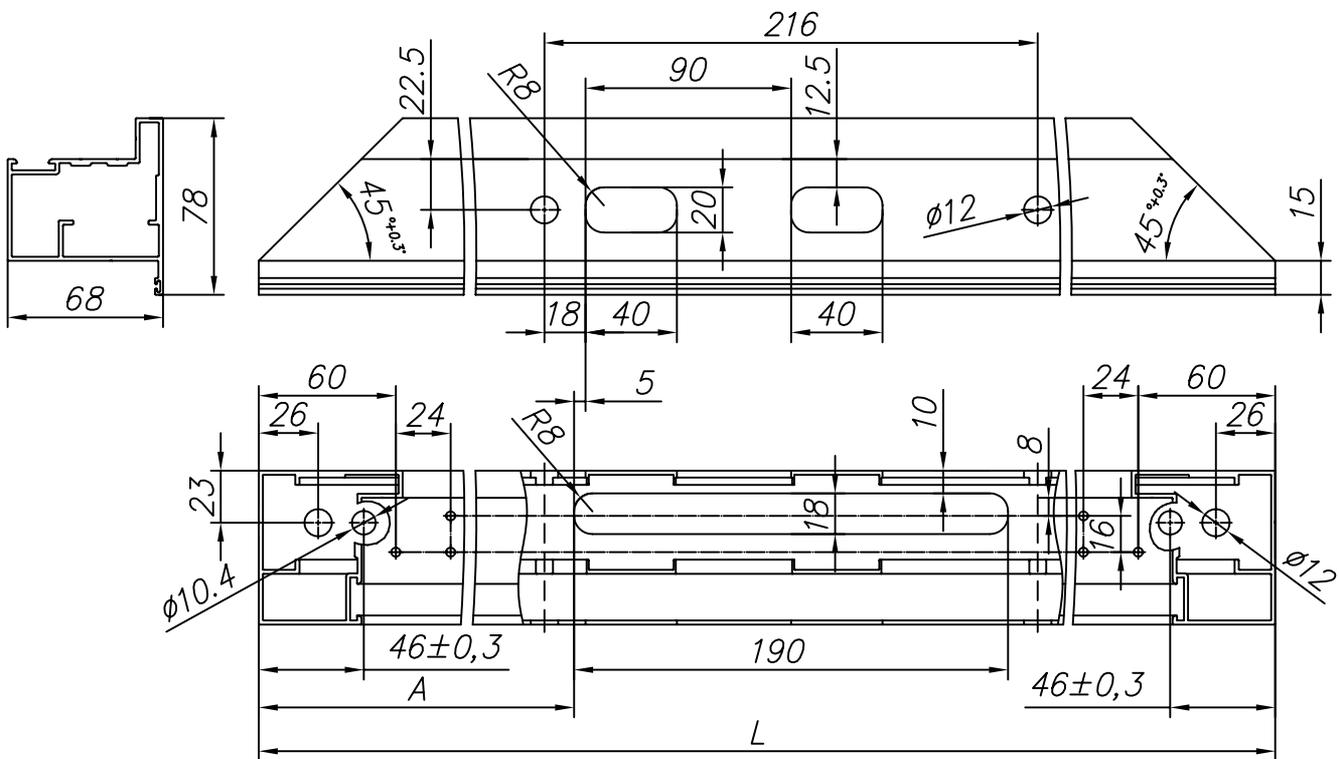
Изготовление стойки с пазом для замка из профиля FLGU 400.0108 (открытие наружу, вправо)
